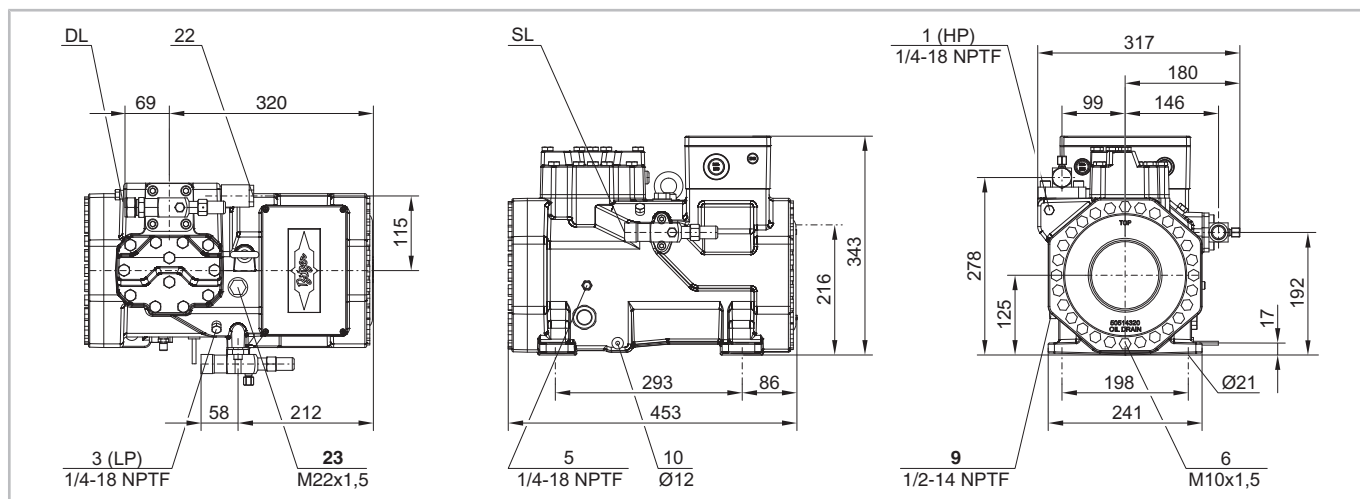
Чертежи с указанием размеров 2MTE-4K .. 2KTE-7K
